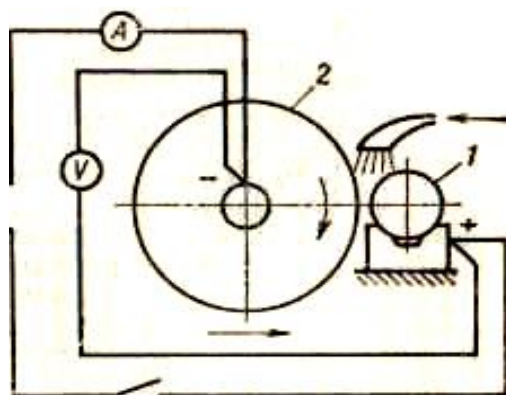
Схема анодно-механічного різання матеріалів
